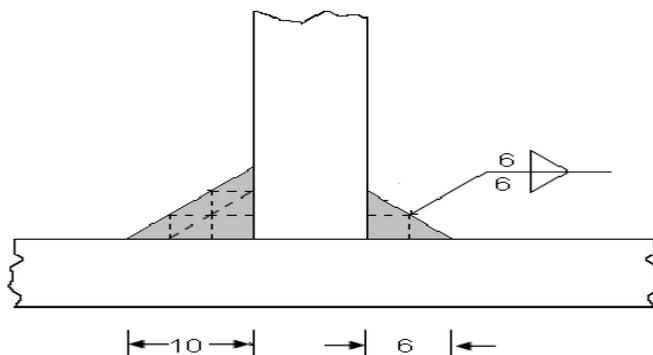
Efectos de la soldadura sobre los requerimientos de metal de aporte para una soldadura de bisel
